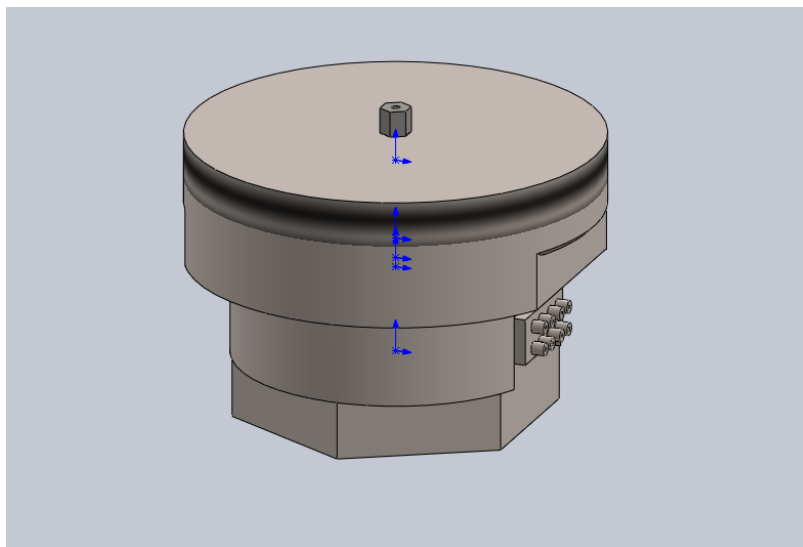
Сборка измерительного модуля датчика и корпуса-крышки
